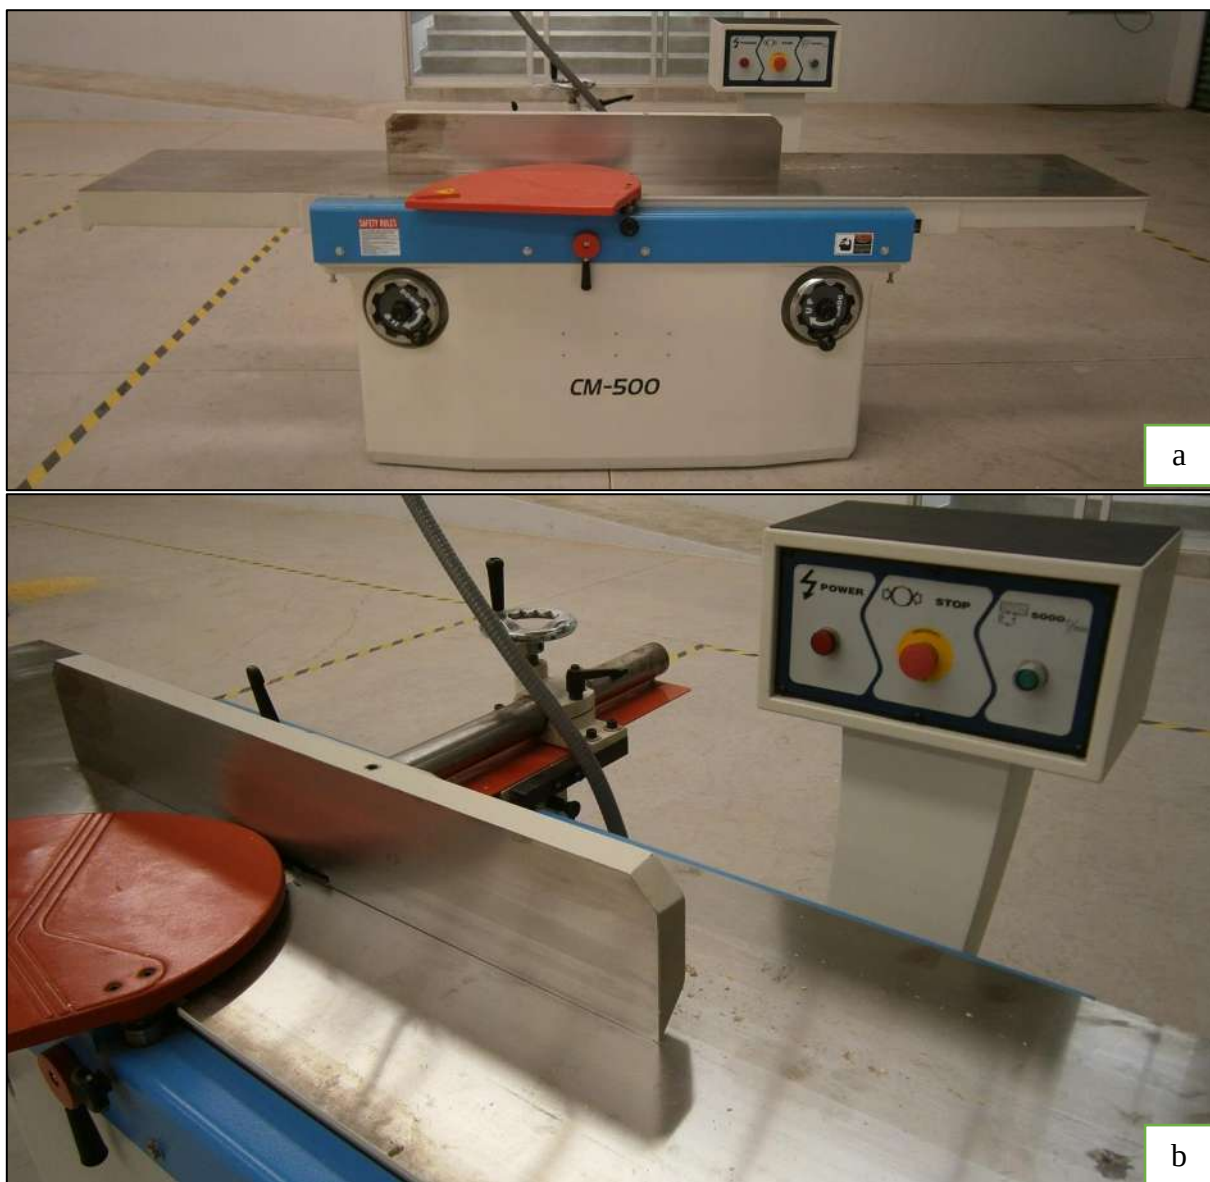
Canteadora CM-500, a) vista frontal, b) vista panel de operación.
